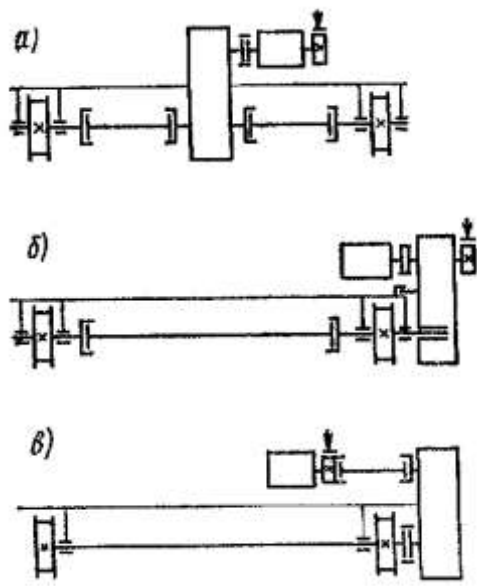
Кинематическая схема механизмов передвижения тележек мостовых кранов: а – с редуктором типа ВК; б – с навесным редуктором типа ВКН; в – с редуктором типа В
